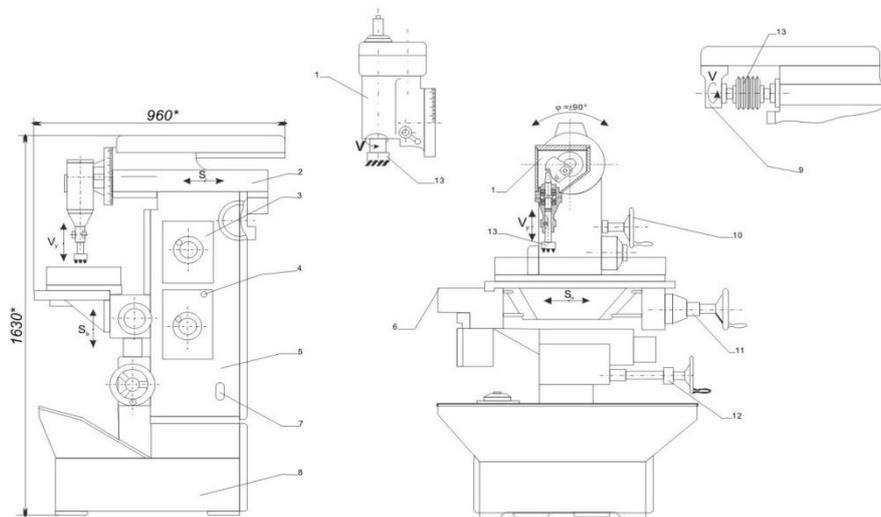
Общий вид виброударного станка для фактурной обработки природного камня.
